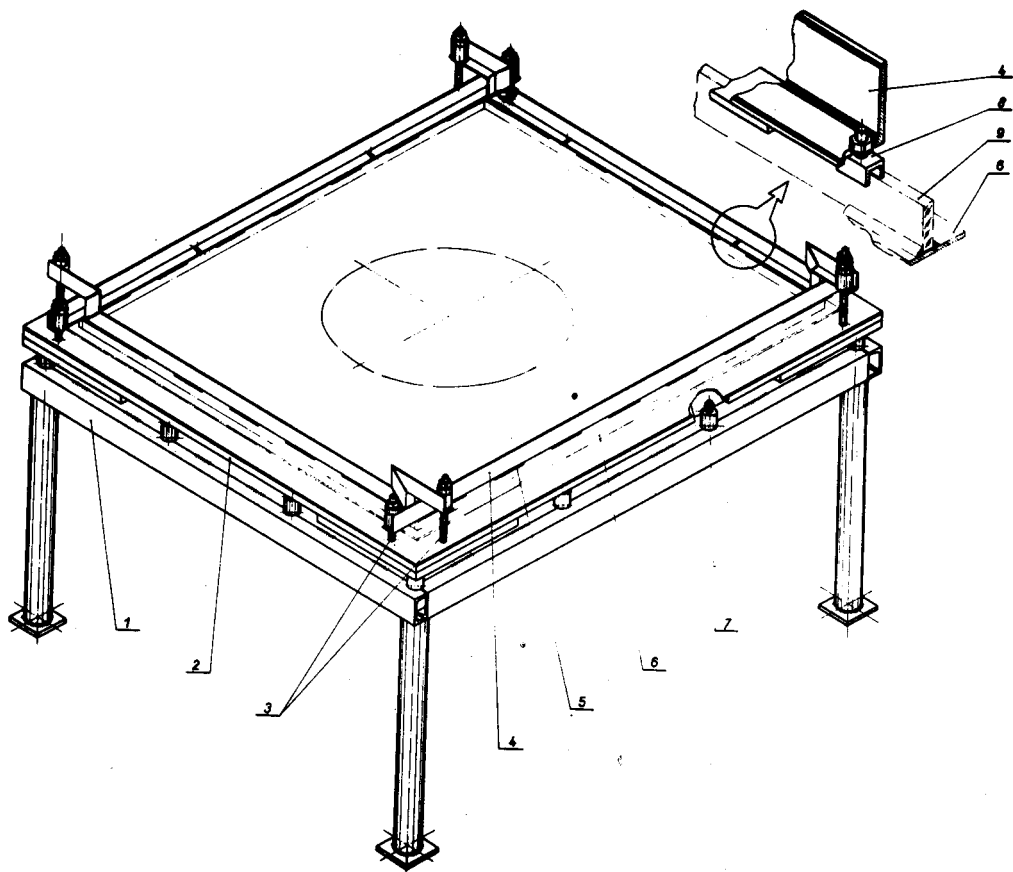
Стол для сборки модуля. 1 - основание; 2 - установочная плита; 3 - болты для крепления прижимных линеек; 4,5 - резиновые прокладки; 6 - электрод; 7 - юстировочные винты для выравнивания плоскости установочной плиты 2; 8 - направляющие вилки; 9 - полоска стекла.
